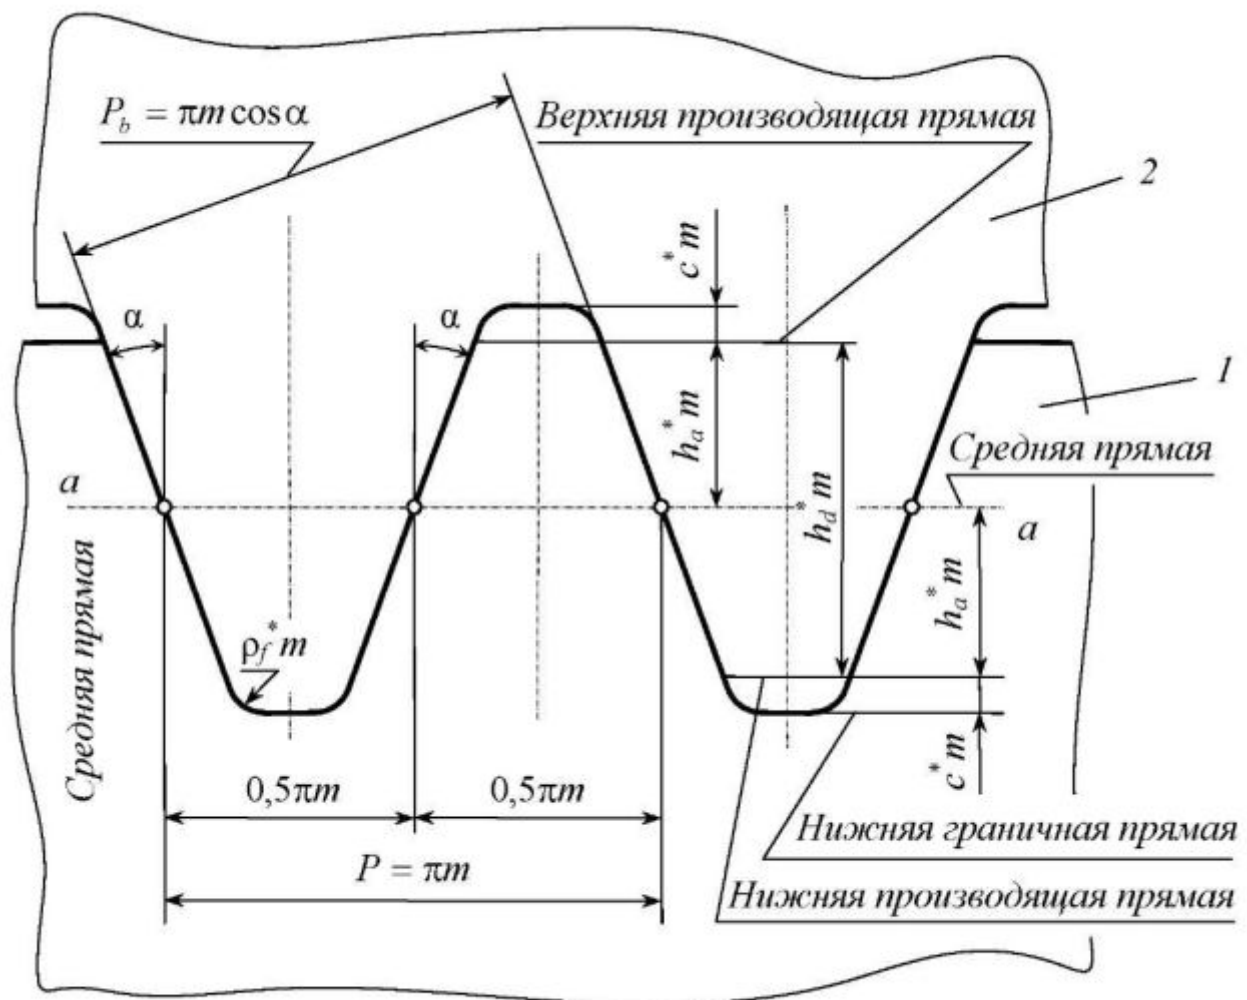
Рабочий контур стандартной инструментальной зубчатой рейки
